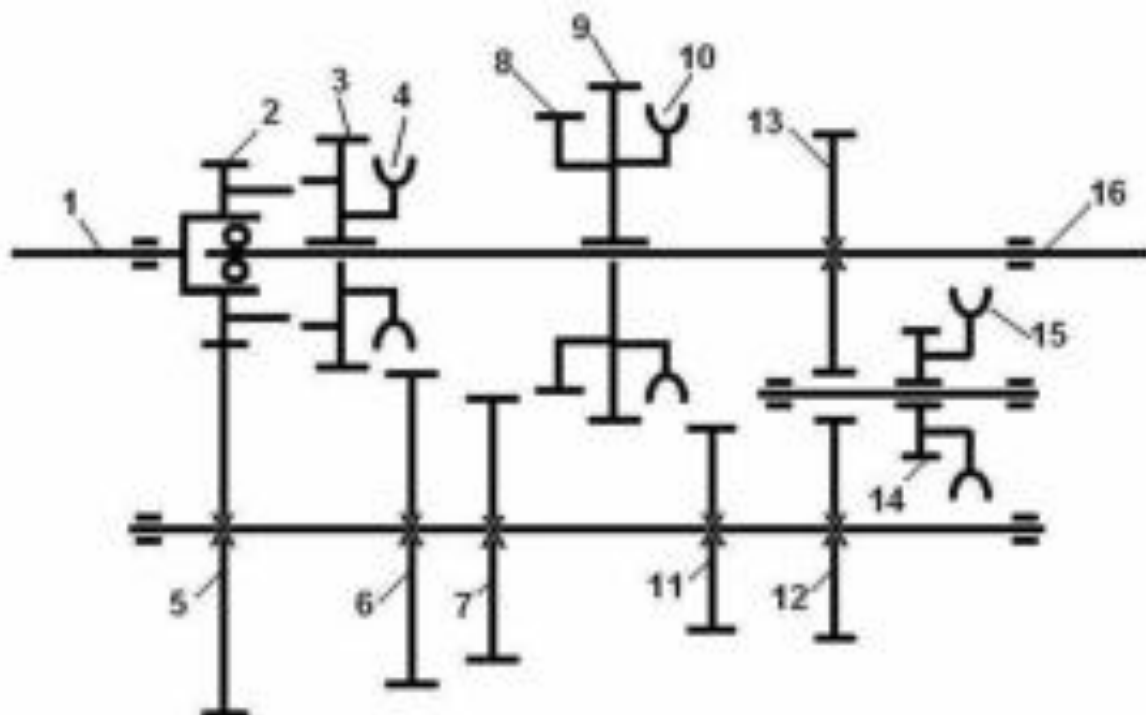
Кинематическая схема четырехступенчатой трехвальной коробки передач.
